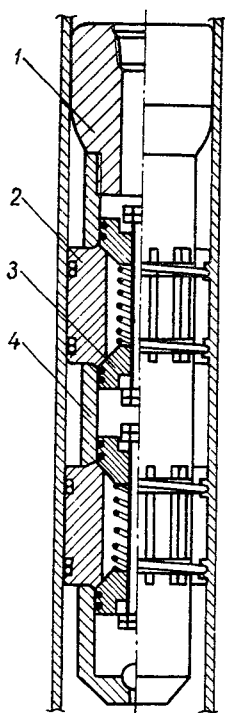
Шаблон-оправка (рабочее положение): 1-шаблон; 2-вкладыш; 3-поршень; 4-корпус.
